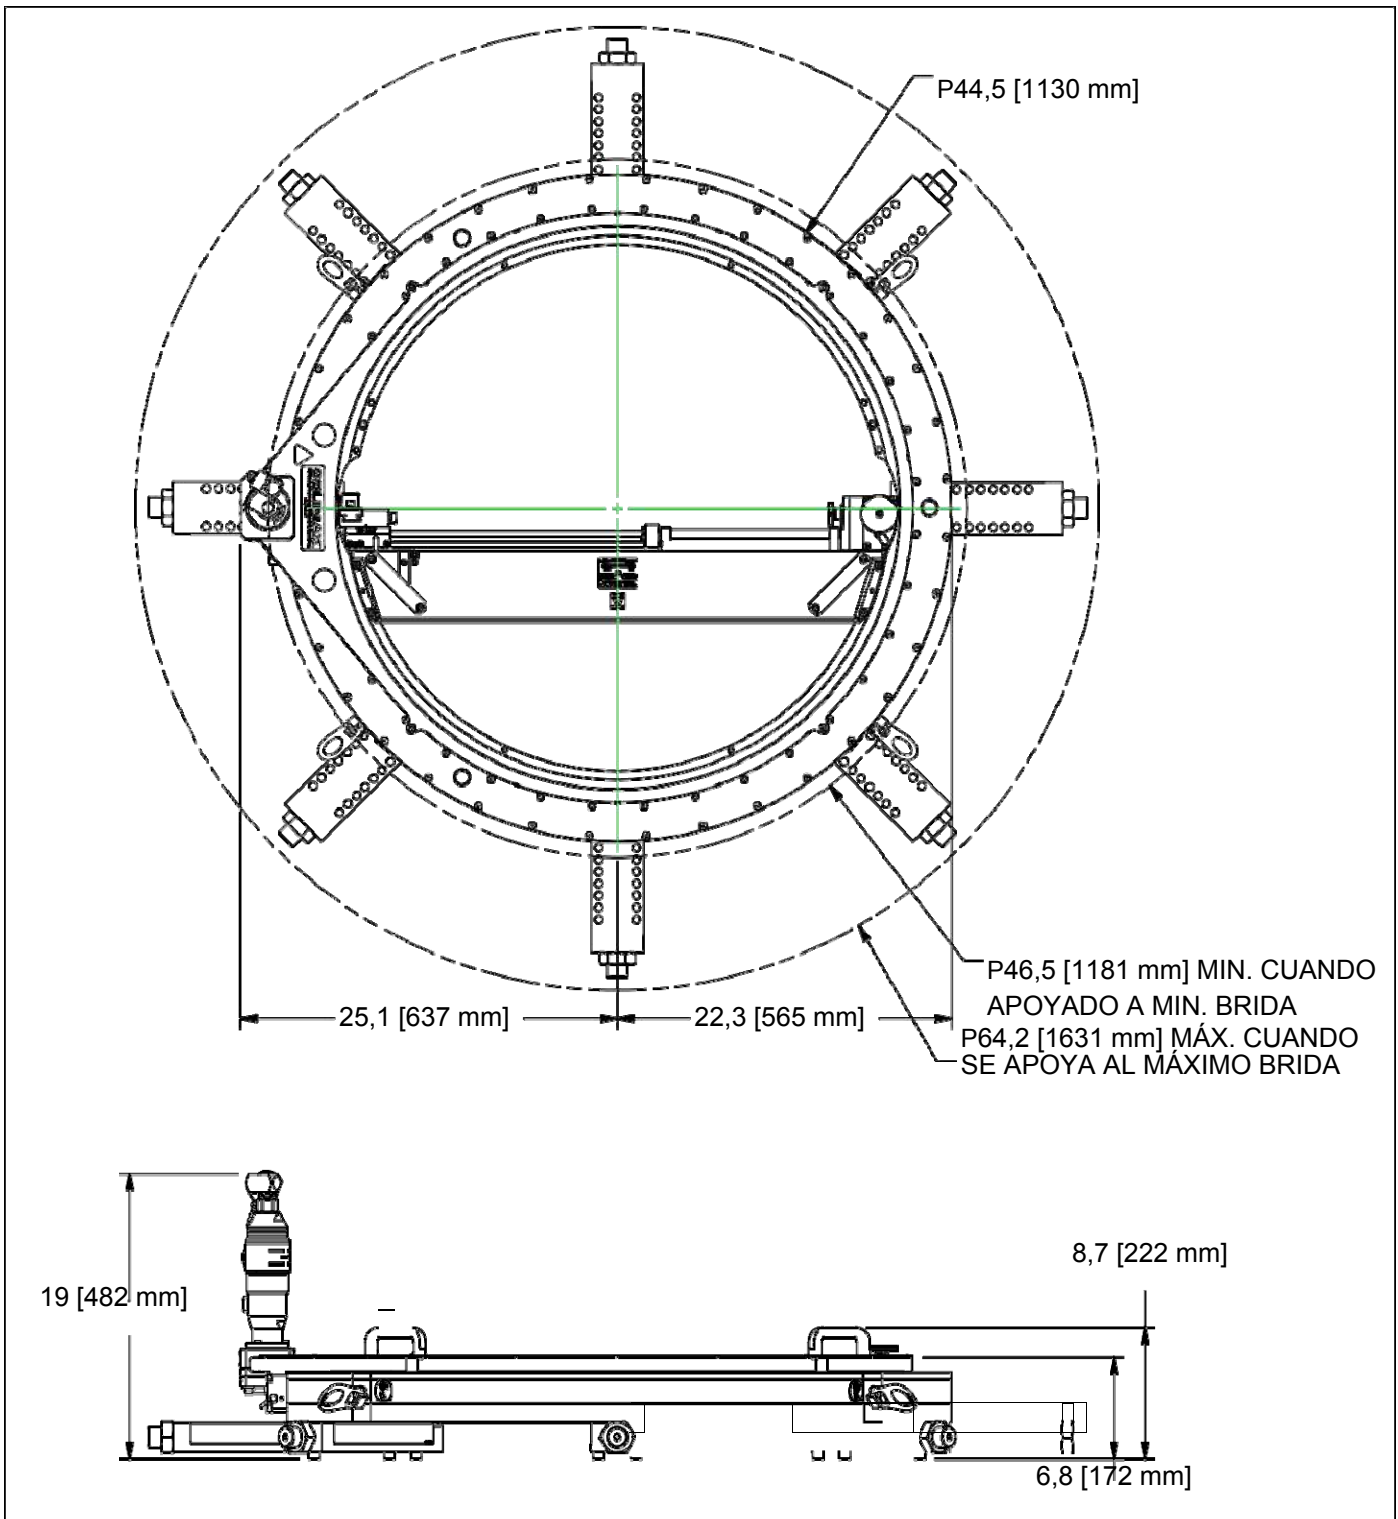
FF3600 DIMENSIONES DE LA MÁQUINA
